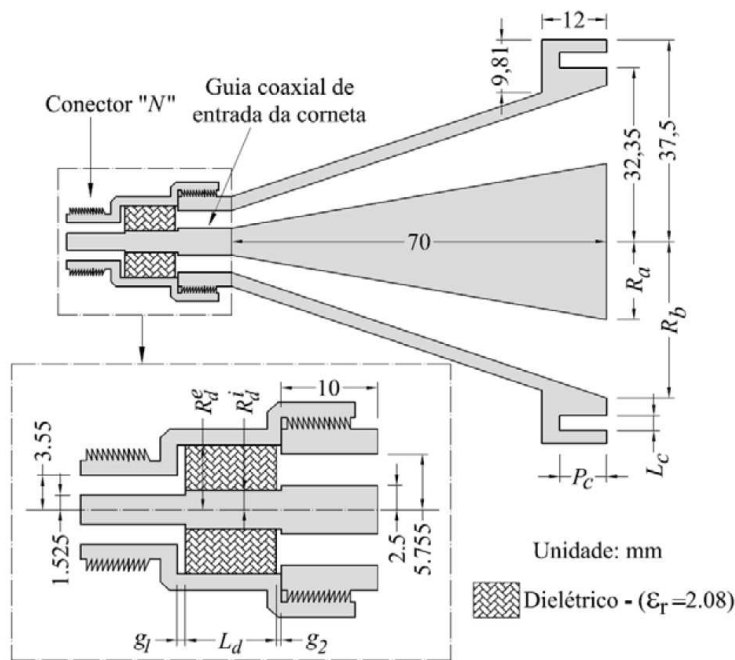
Dimensões da corneta coaxial apresentada por [12]. Imagem obtida em [13, p. 229].
